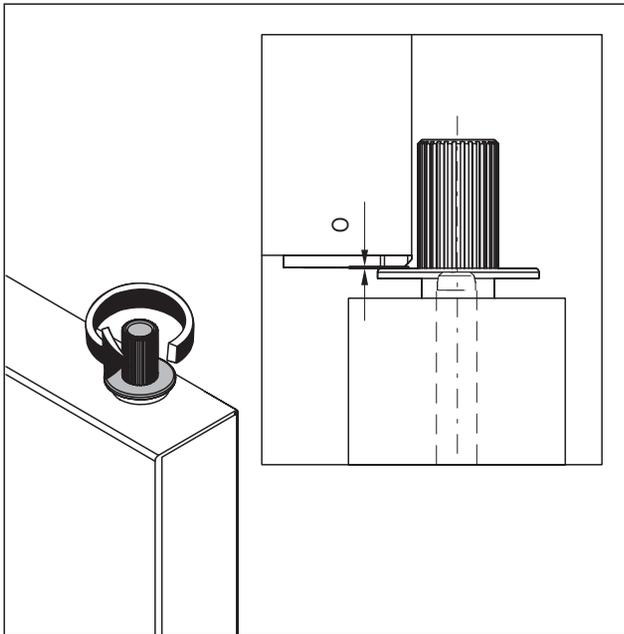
Teller in der Mitte des Einstellwerkzeug bündig mit Stangenschließblech
